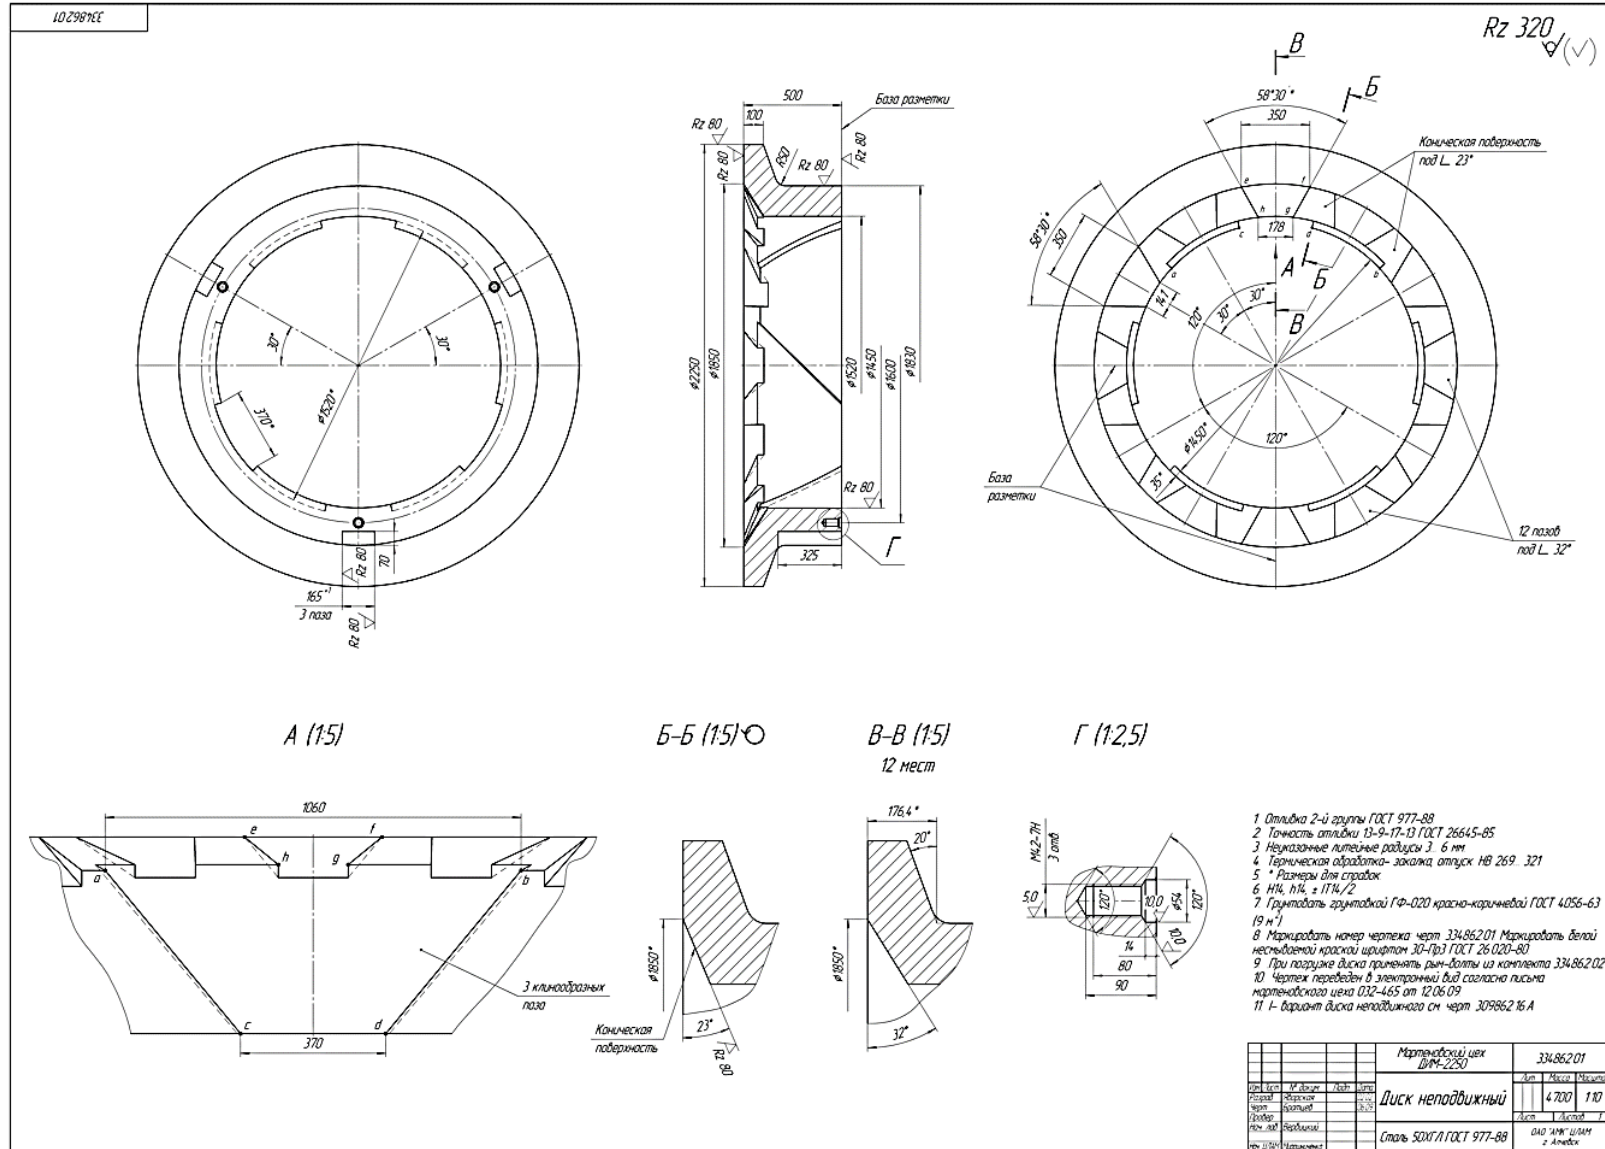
Копия рабочего чертежа неподвижного диска
